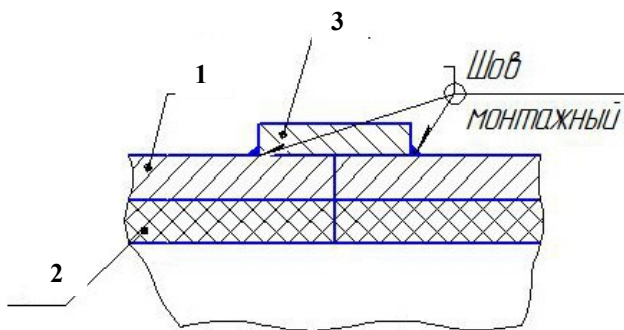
Неразъемное соединение труб с керамическим покрытием при помощи бандажей.
